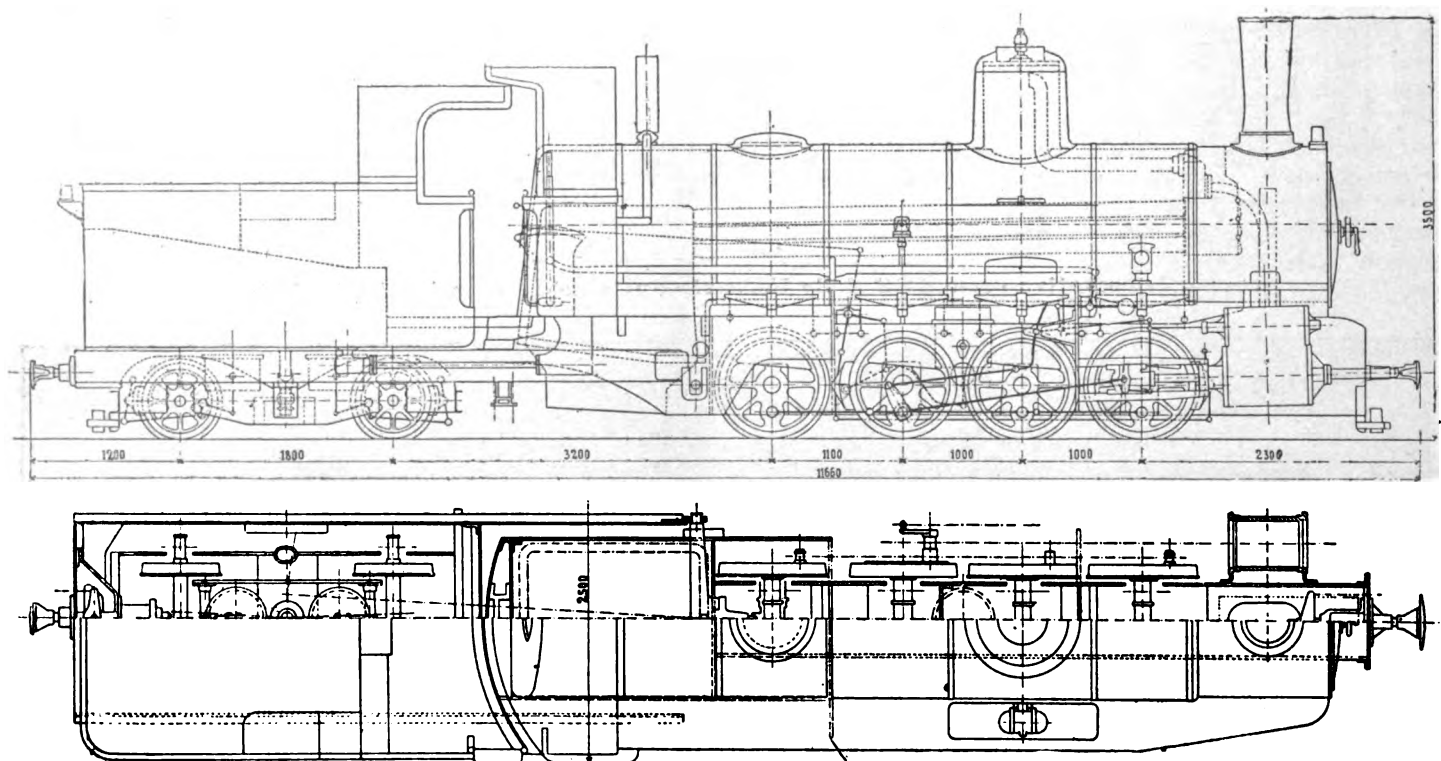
e 10 — Locomotiva serie 178 delle Ferrovie austriache. — Elevationi e pianta.
